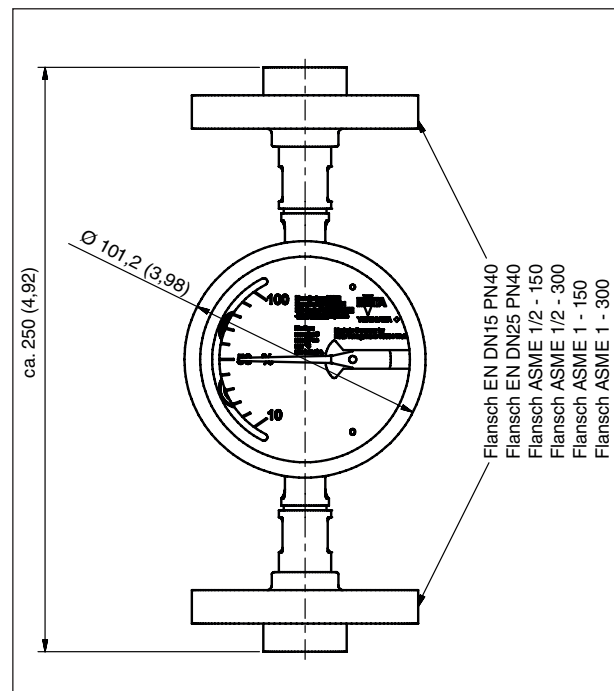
Ausführung mit Flanschanschlüssen, Abmessungen in mm (Zoll)
